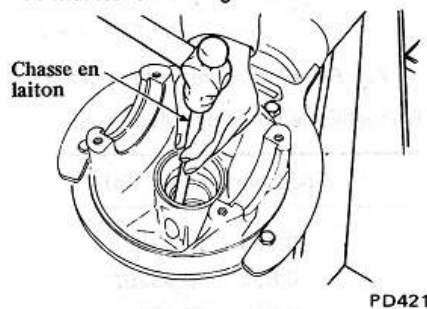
Dépose des cuvettes des roulements avant et arrière du pignon
